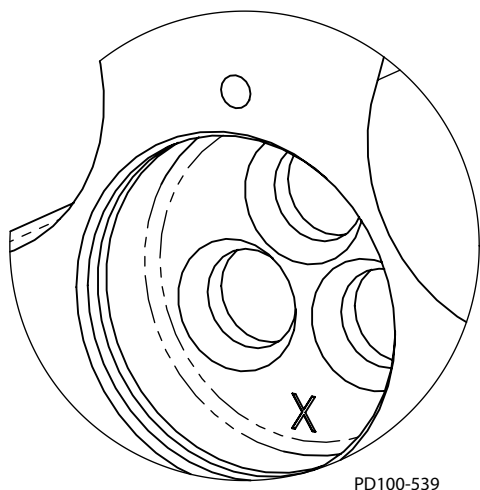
Pumpenabdeckung und Rotor entfernen
